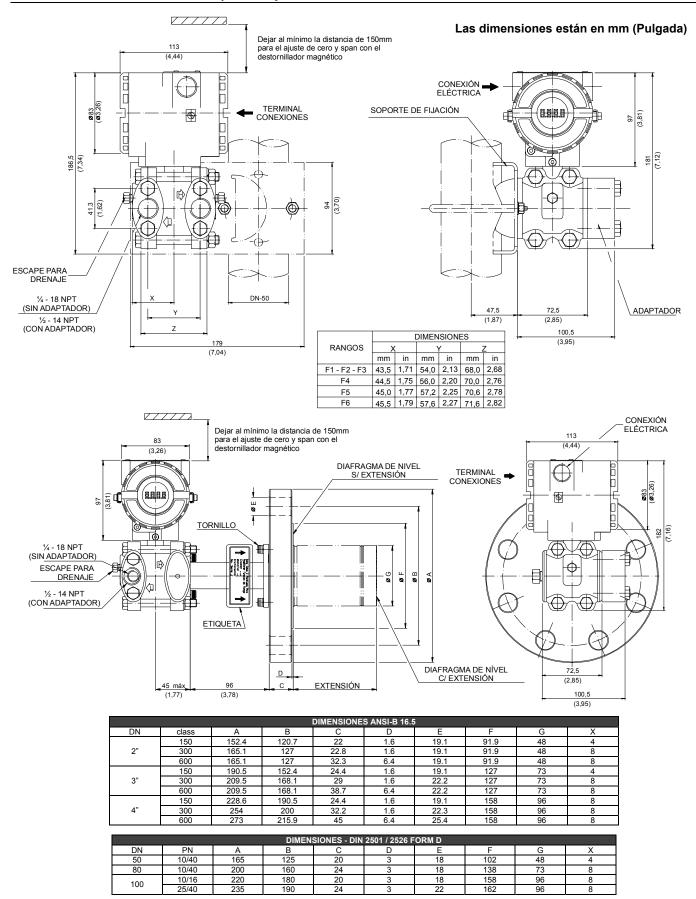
Diseño Dimencional de Montaje del LD301
